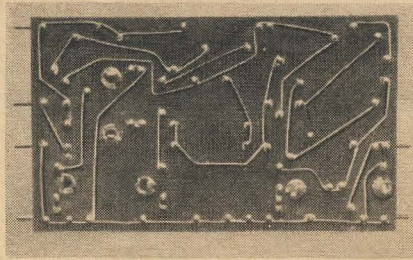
Rückansicht der verdrahteten Drahtstift-platte
